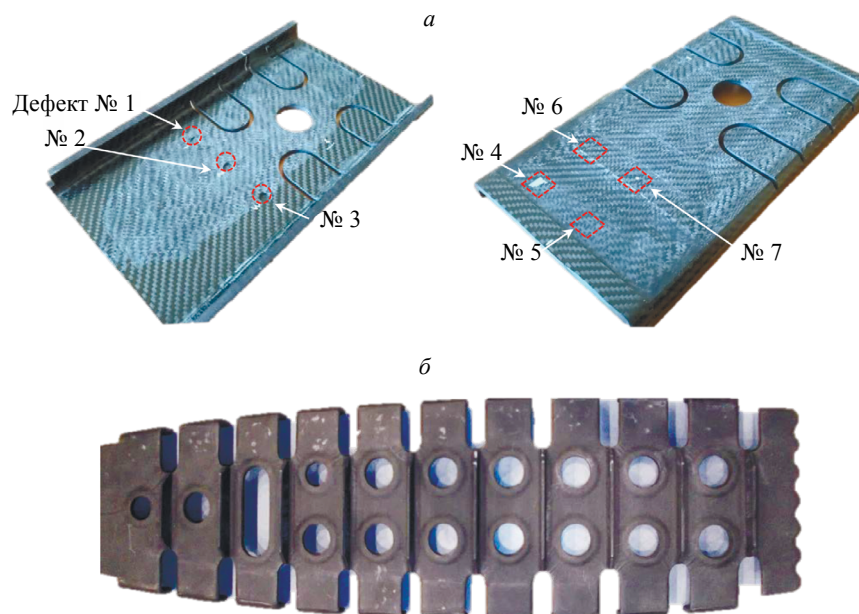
Стандартный образец из углепластика (а), изготовленный из 25-и слоев углеродной ткани с элементами формы, соответствующими нервюре цельнокомпозитного самолета ТВС-2ДТС (СибНИА им. С.А. Чаплыгина) (б).
